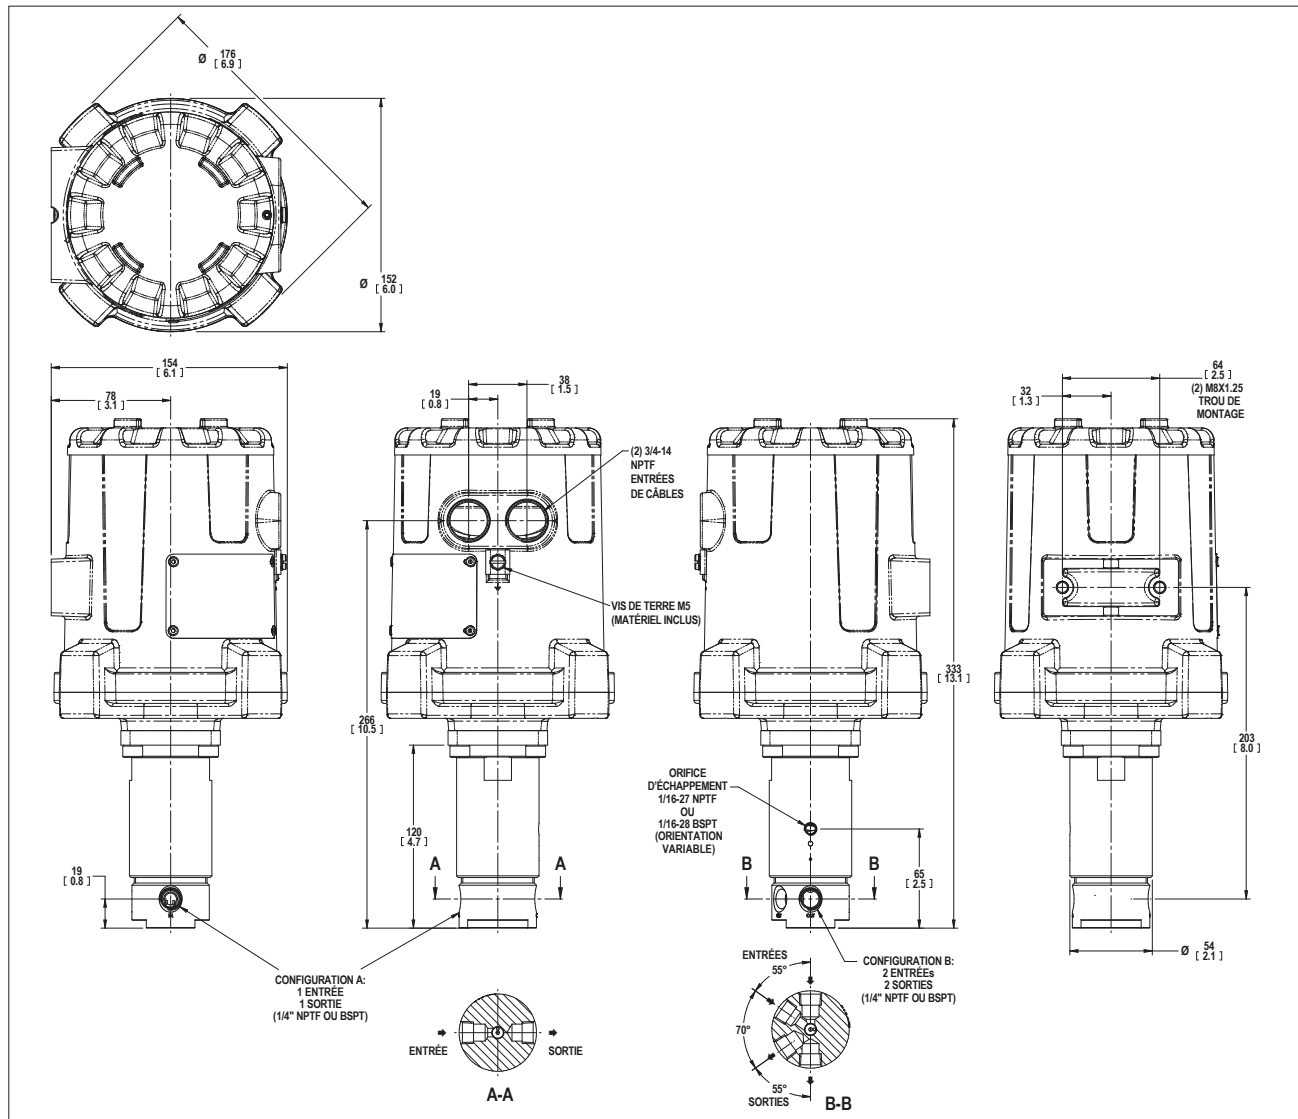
Dimensions d'installation de la motorisation PAX1 et du régulateur de pression modèle HPD ou HPP
